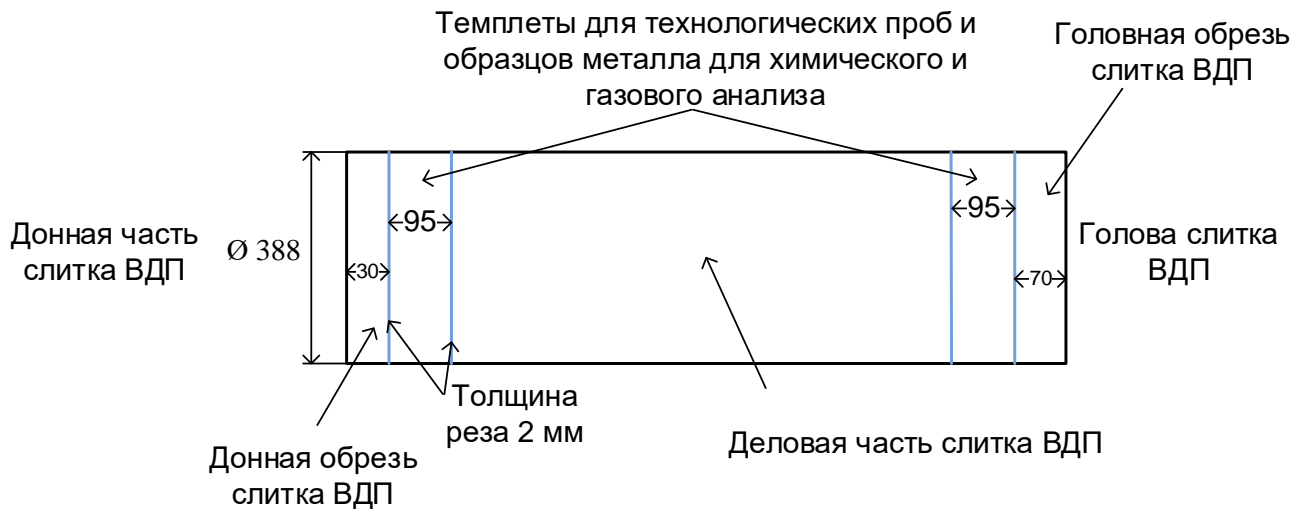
Схема порезки слитка B192-36 сплава Inconel 718
